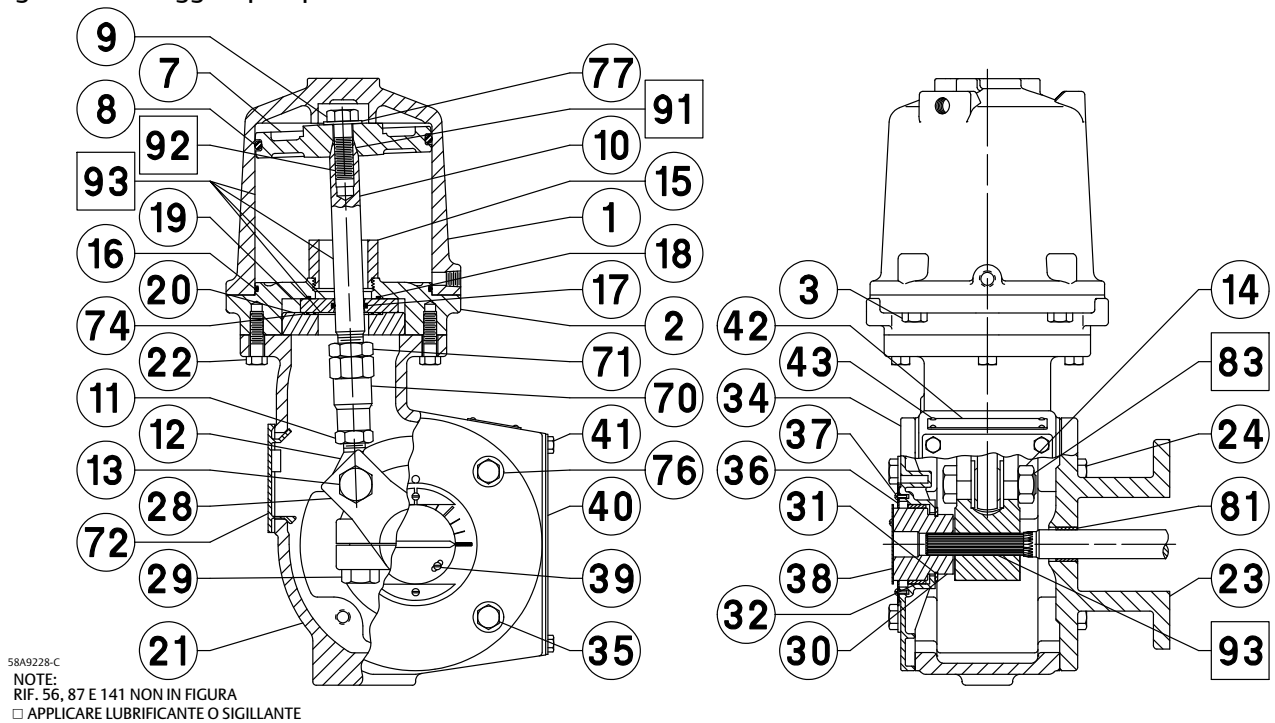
Montaggio tipico per attuatori Fisher 1061 dimensioni 80 a 100
